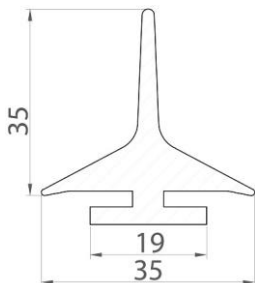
Профиль уплотнительный для установки по контуру маятниковых дверей
